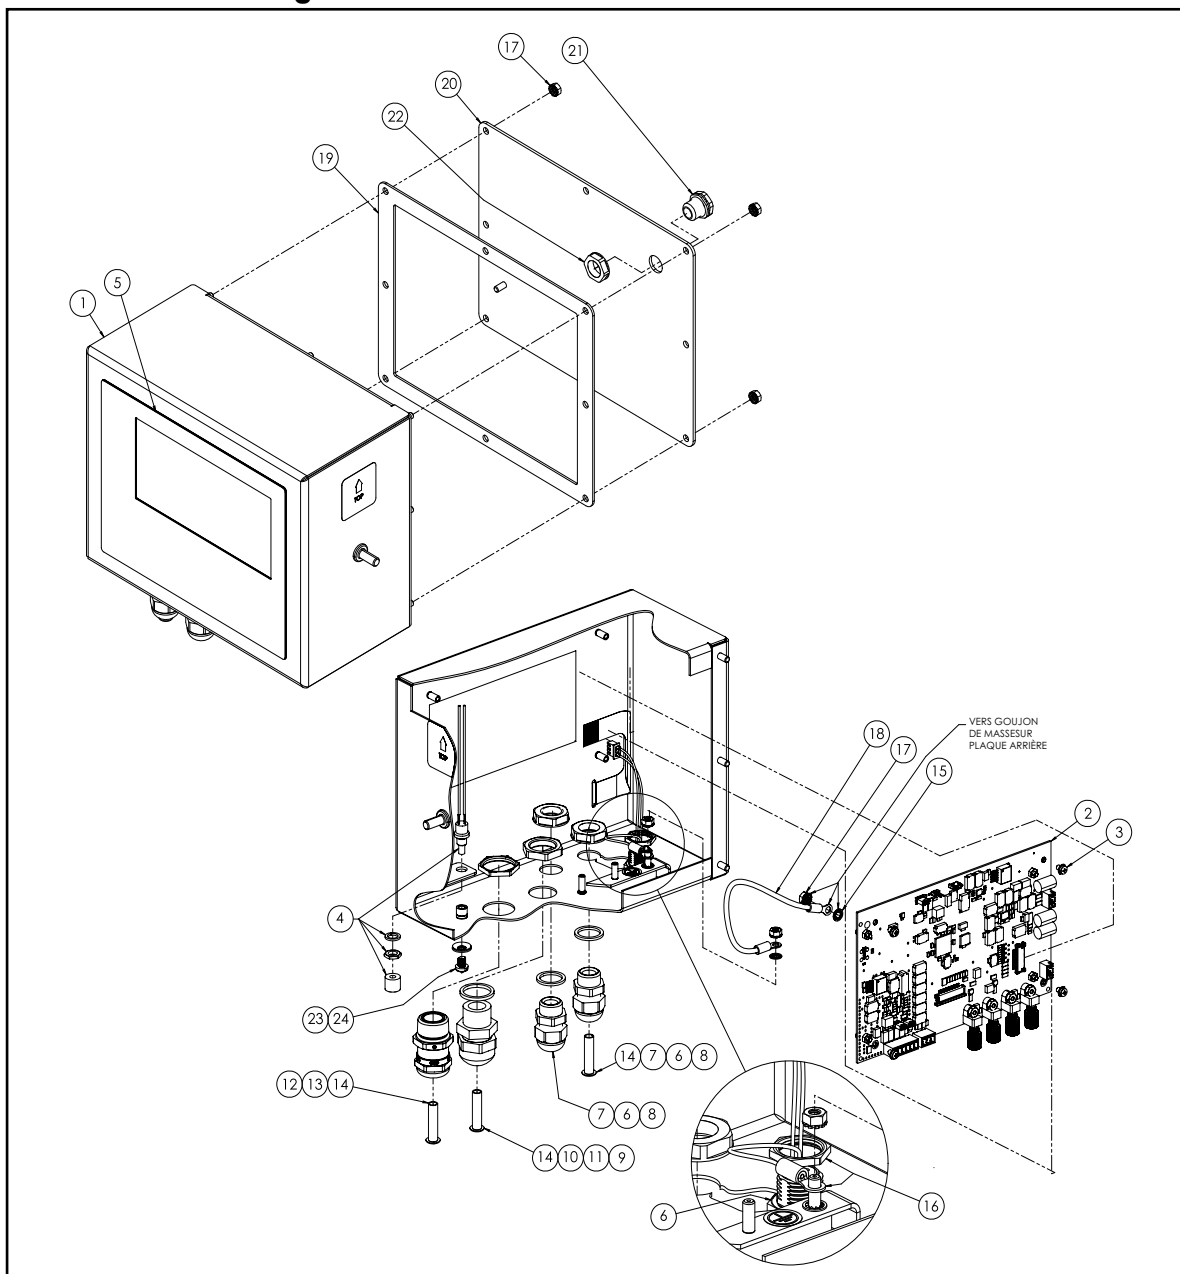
Vue éclatée des pièces de l'indicateur 882IS
